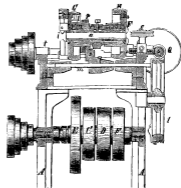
Krone's Façon-Drehbank. Grundriß.
